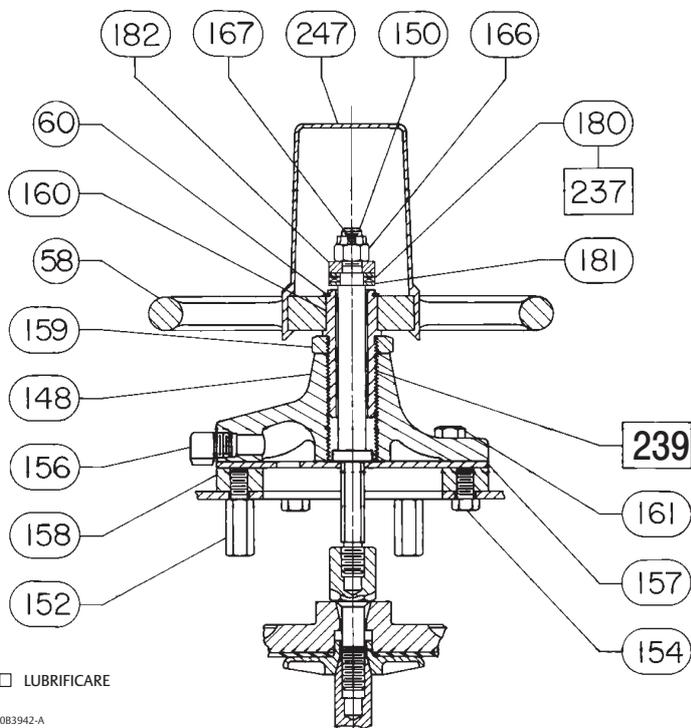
Volantino di testa per attuatori di dimensioni 70 e 87
